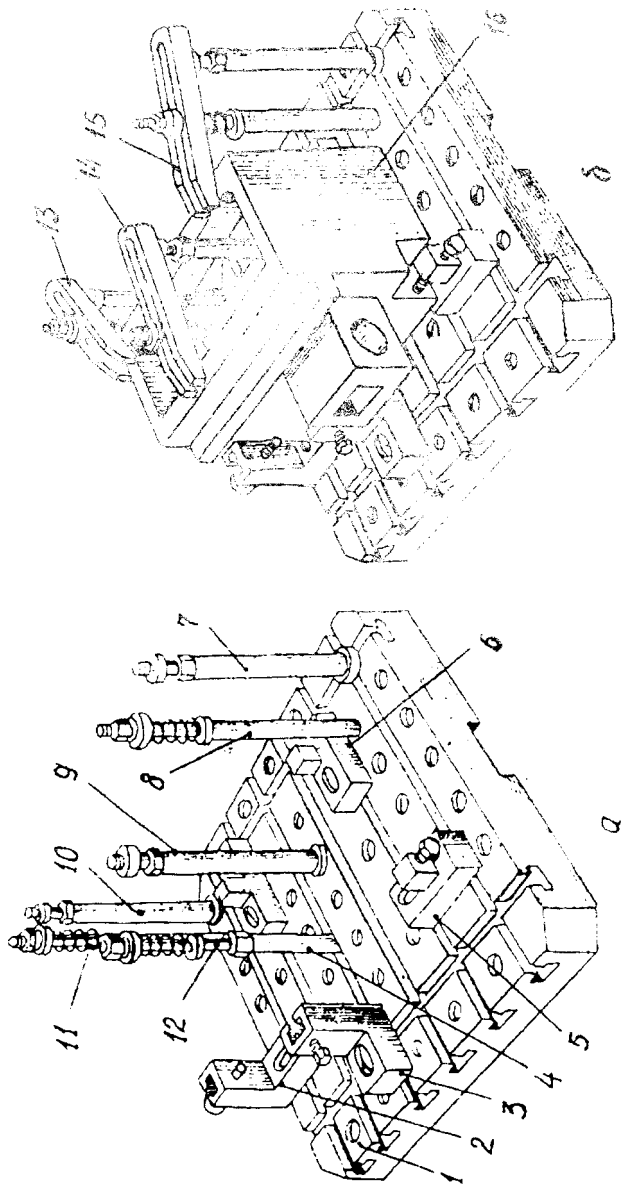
Приспособление-спуитник: а - плита с 6-ю рядами 4-х рядовыми отверстиями; б - приспособление-спуитник
